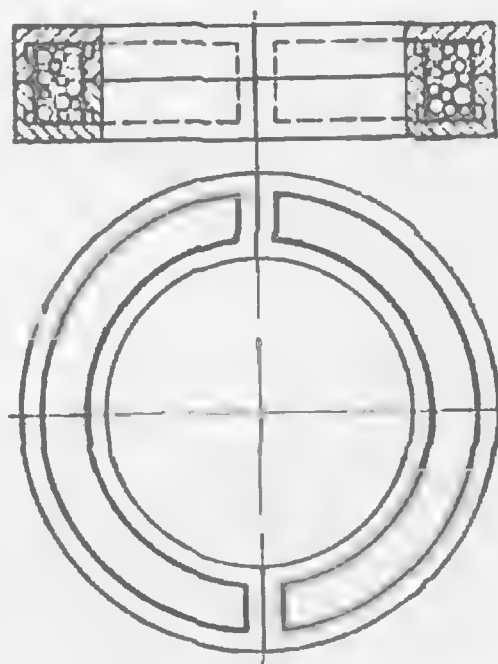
Конструкция металлопластического уплотнительного кольца фирмы Дюранс.
